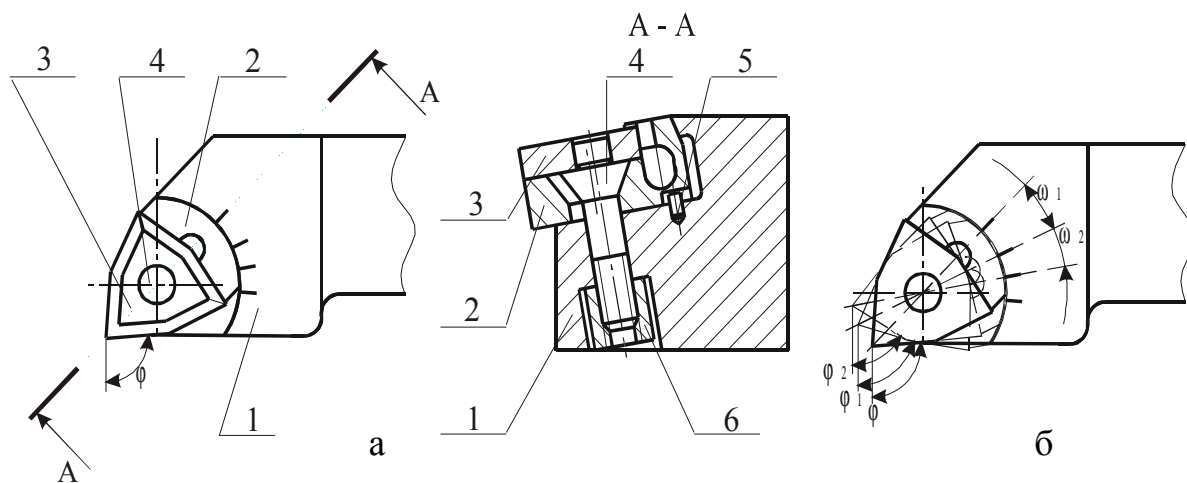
Універсально-збірний різець з поворотною робочою частиною:
